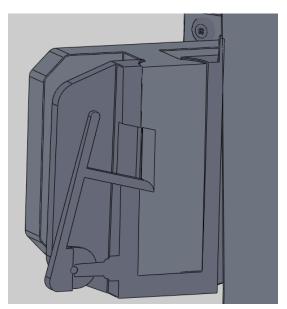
Vista corte unión mecanismo estructurarespaldo.
